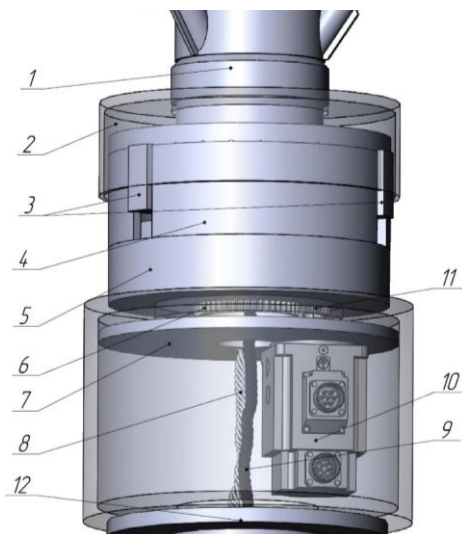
Электромеханический блок торможения, интегрированный в ступицу ВЭУ-3: 1 – ступица; 2 – контактная стенка; 3 – кулачки; 4 – корпус с направляющими; 5 – волновой редуктор; 6 – входной вал (шестерня) редуктора; 7 – установочная шайба; 8 – гибкий трос ручного привода; 9 – провод от генератора; 10 – электрический привод; 11 – приводная шестерня; 12 – фланец мачты
